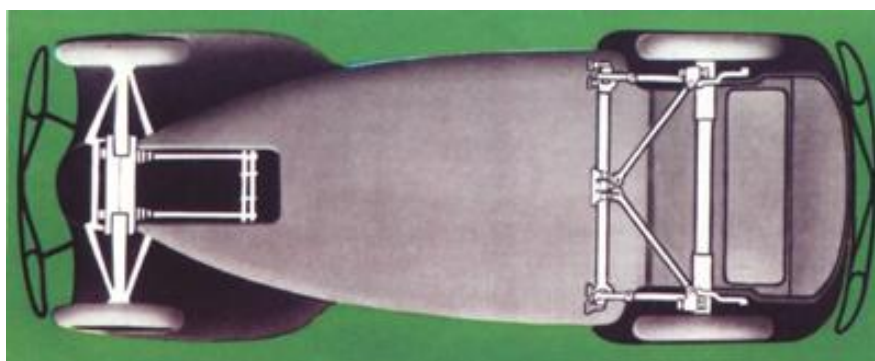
Odpružení přední nápravy torzními tyčemi v kombinaci s teleskopy [34]
